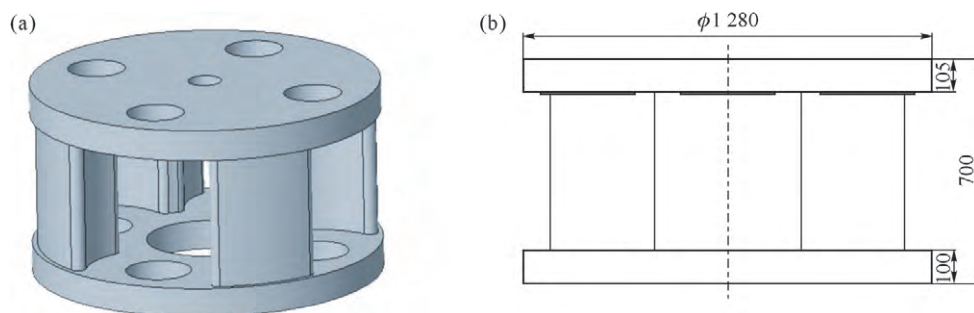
铸件几何形状和主要尺寸:(a) 铸件形状,(b) 铸件主要尺寸
